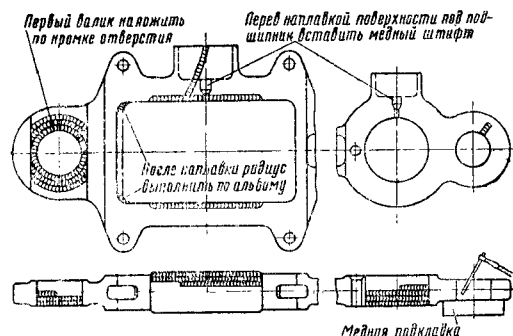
Литая надрессорная балка тележки, отремонтированная сваркой: а—заваренные трещины; б—наплавленный борт паза; в—заваренное отверстие
